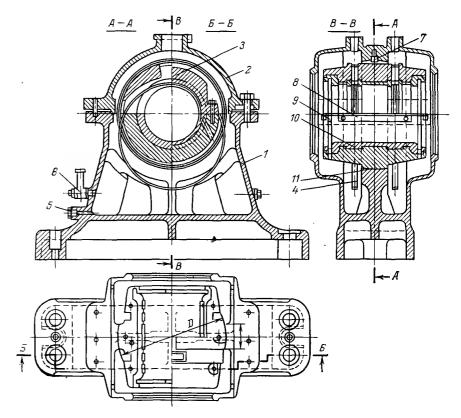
Стояковый подшипник с кольцевой смазкой
